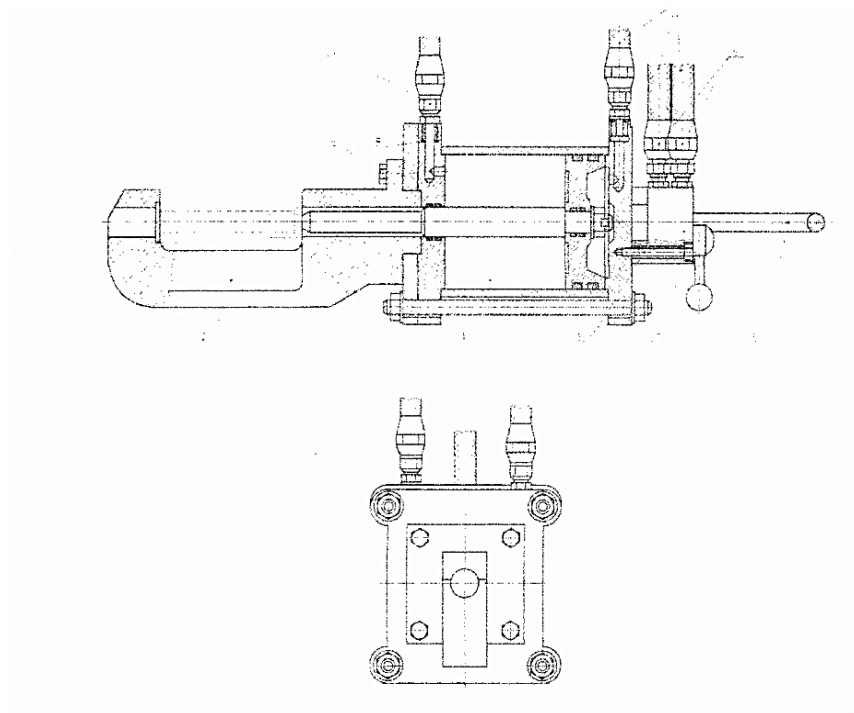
Пристрій для випресовки (запресовки) шворнів:
